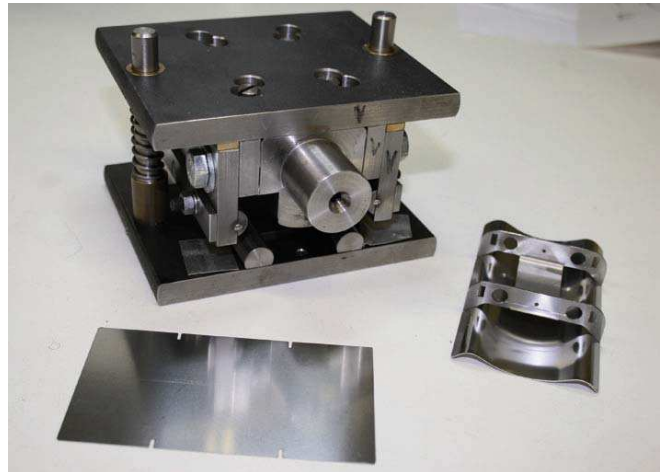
Tiefziehwerkzeug für Quadrupol-Linse
